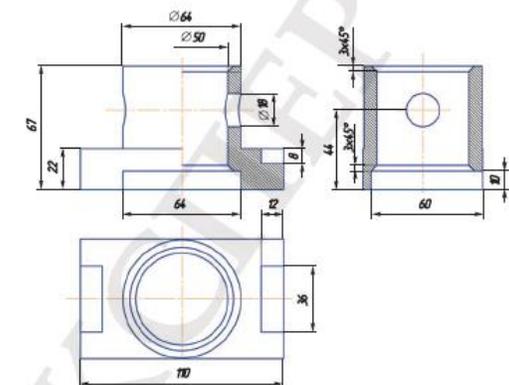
Патрубок.cdw. Чертеж с разрезами
